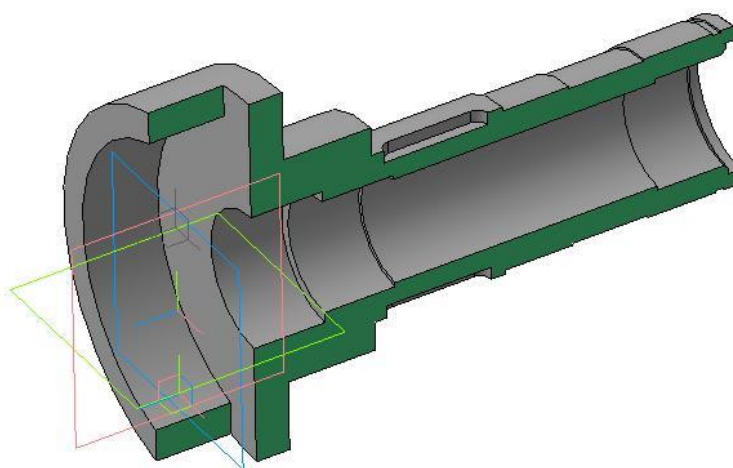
Твердотельная модель детали «Корпус фрикционной муфты»
